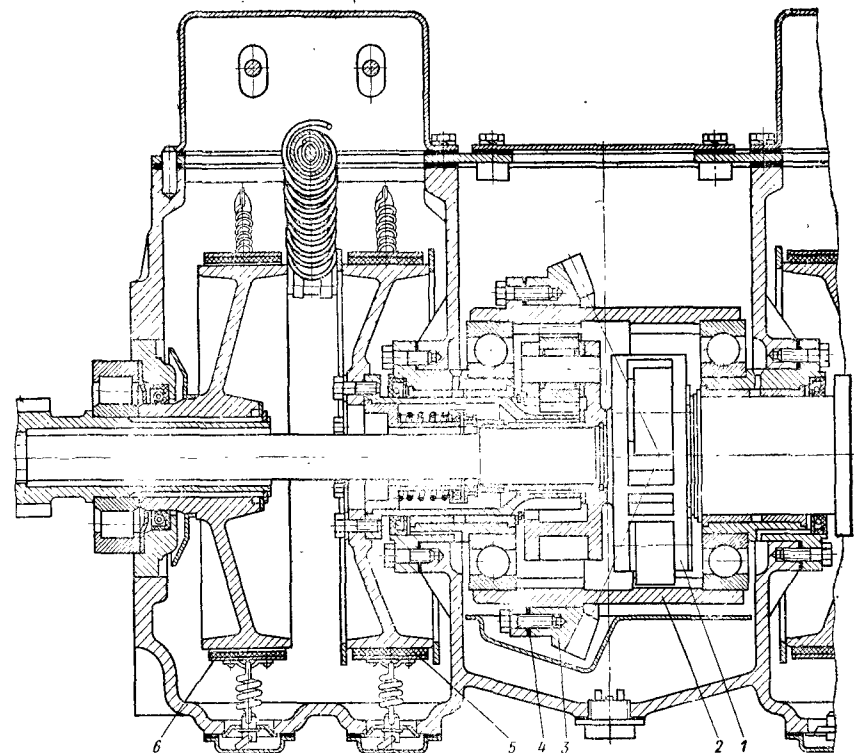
Планетарный механизм поворота трактора ДТ-75:
